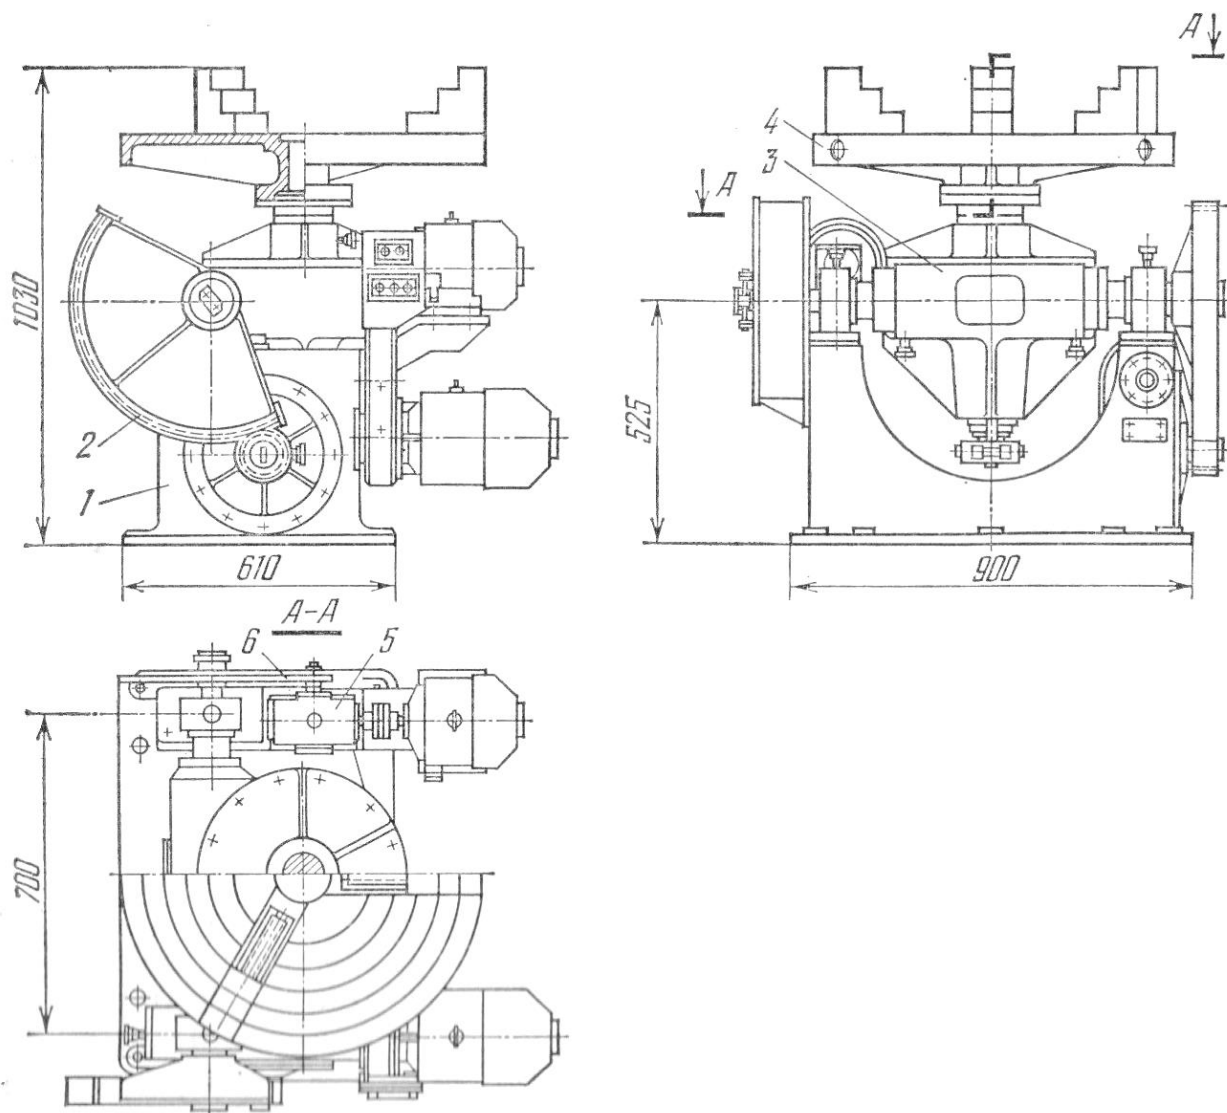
Сварочный манипулятор Т – 25М: 1 – станина; 2 – механизм наклона;
